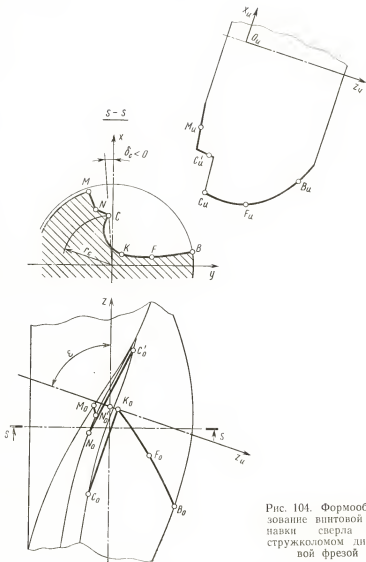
Формообразование винтовой канавки сверла со стружколомом дисковой фрезой
